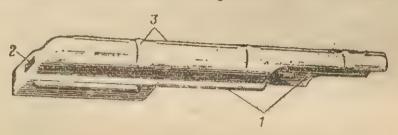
Крышка ствольной коробки: 1 - ступенчатый вырез; 2 - отверстие; 3 - ребра жест-
